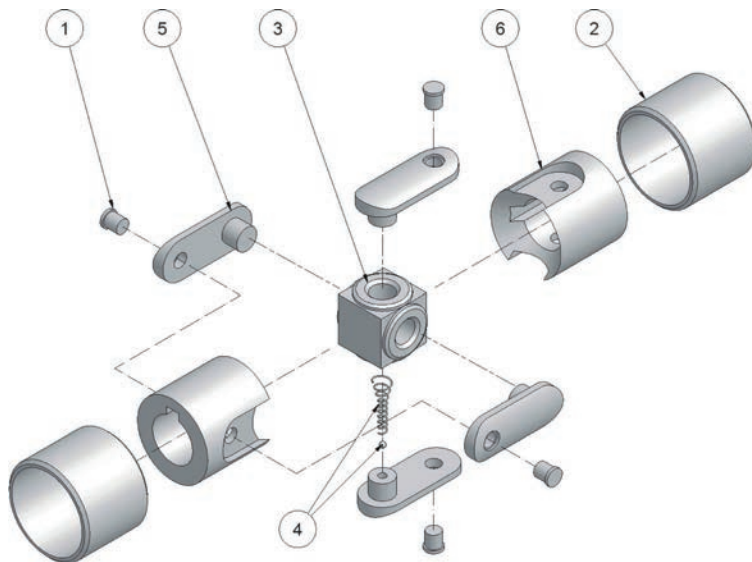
Explosionszeichnung Wellengelenk Laschenausführung Serie S
